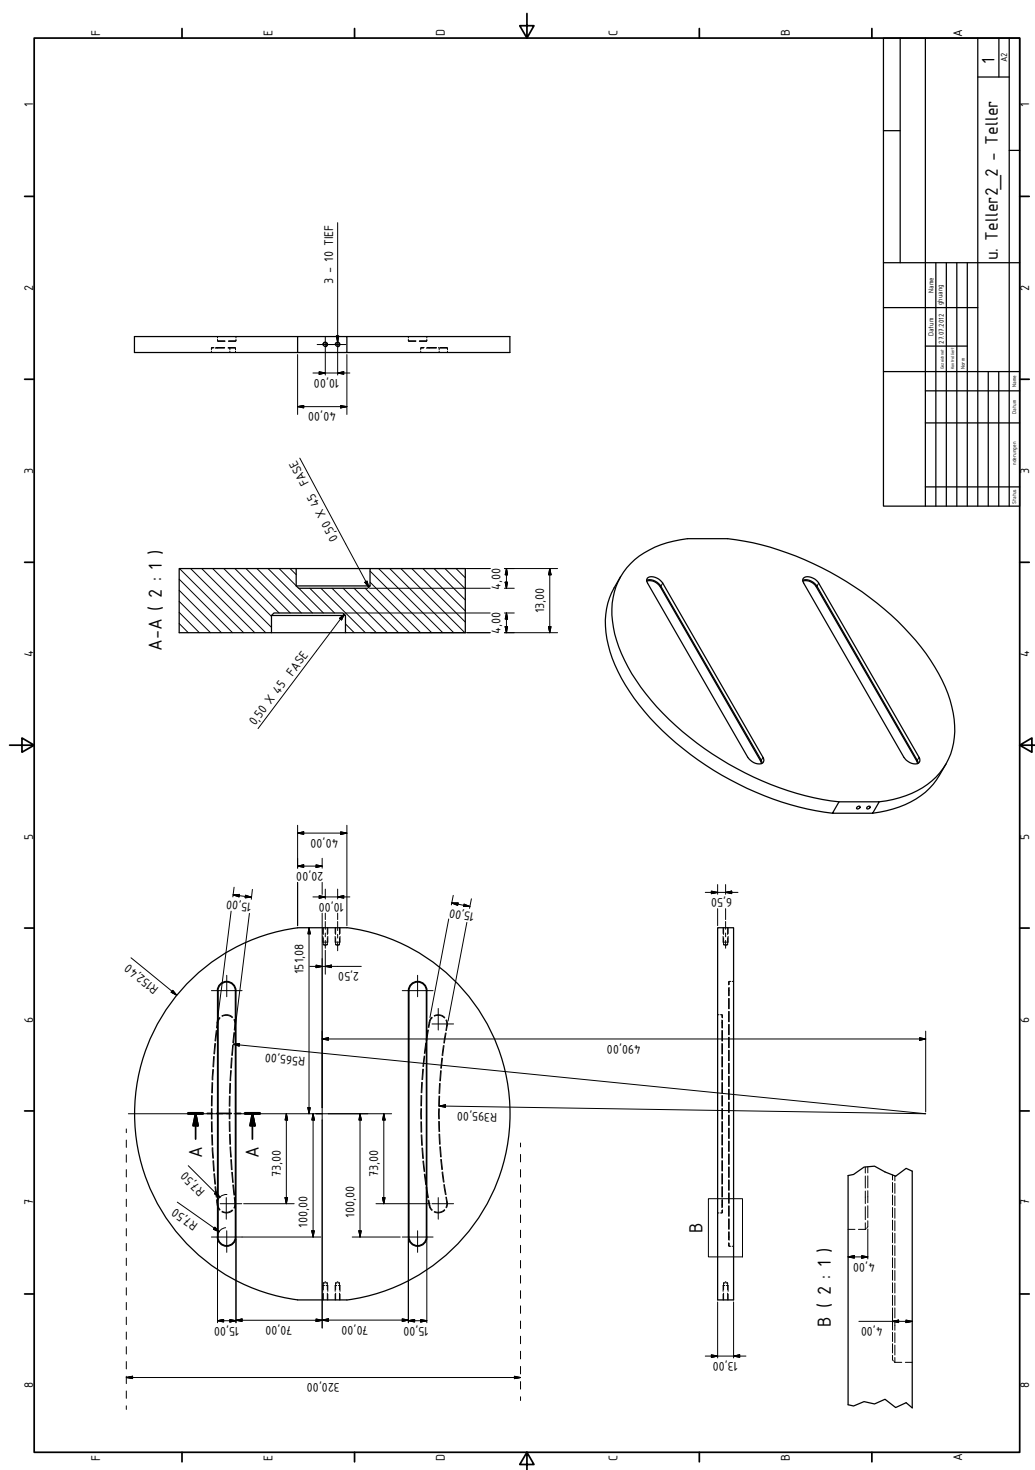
Technische Zeichnung der mittleren Platte: Diese wird auf die untere Platte gelegt, sodass sie sich nach links und rechts bewegen kann.
